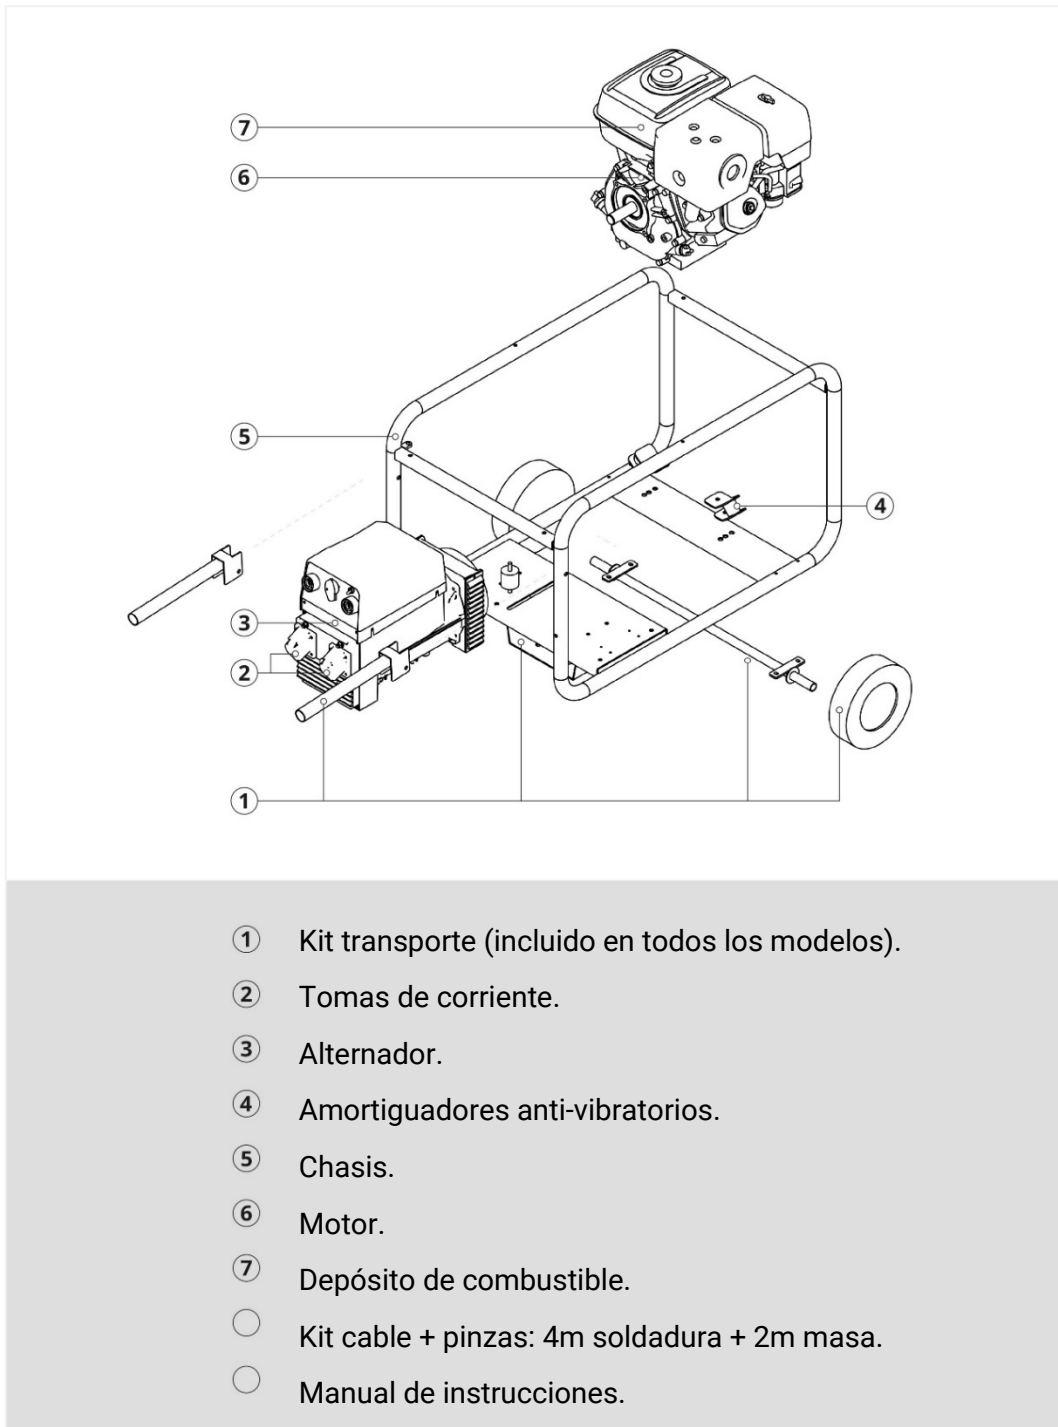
Despiece general de una motosoldadora – genérica - de la gama Portátil.
